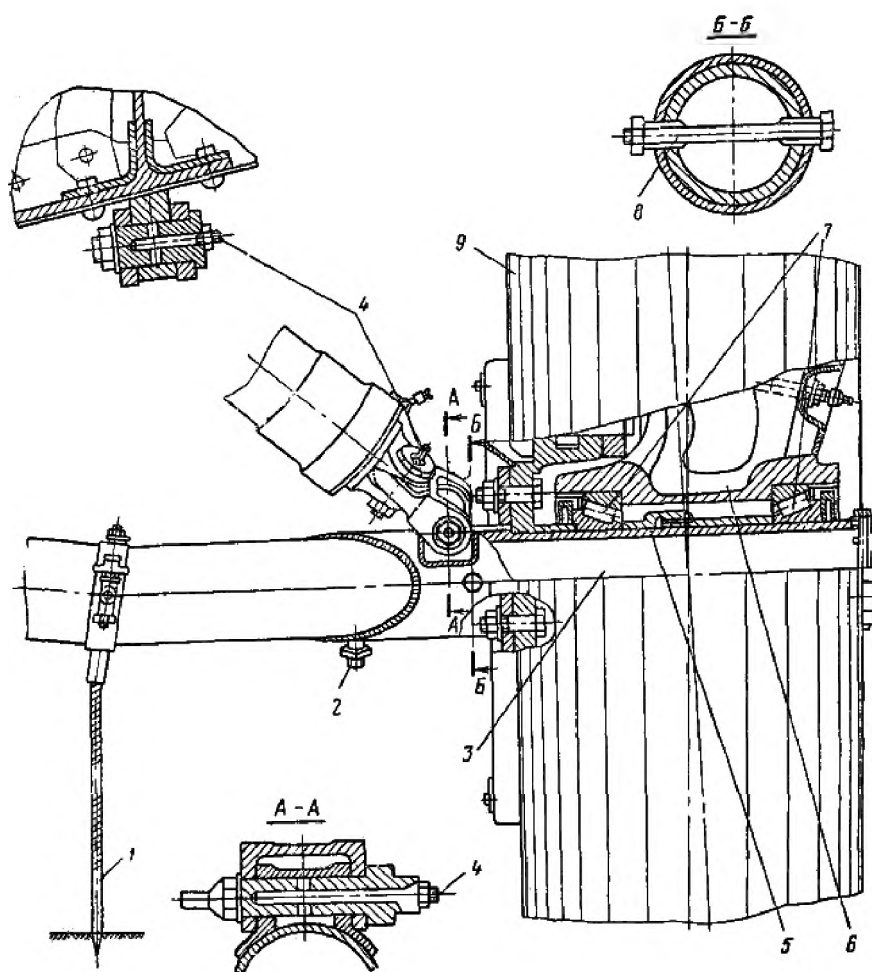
Устройство колеса главной стойки шасси вертолета Ми-2 [12]:
